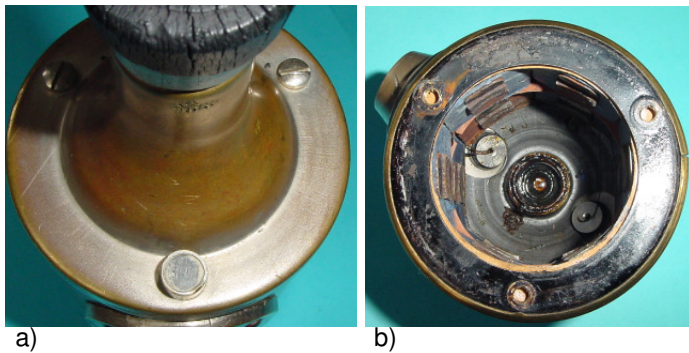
Befestigung des Lagerhalses am Gehäusetopf mit drei Schrauben
